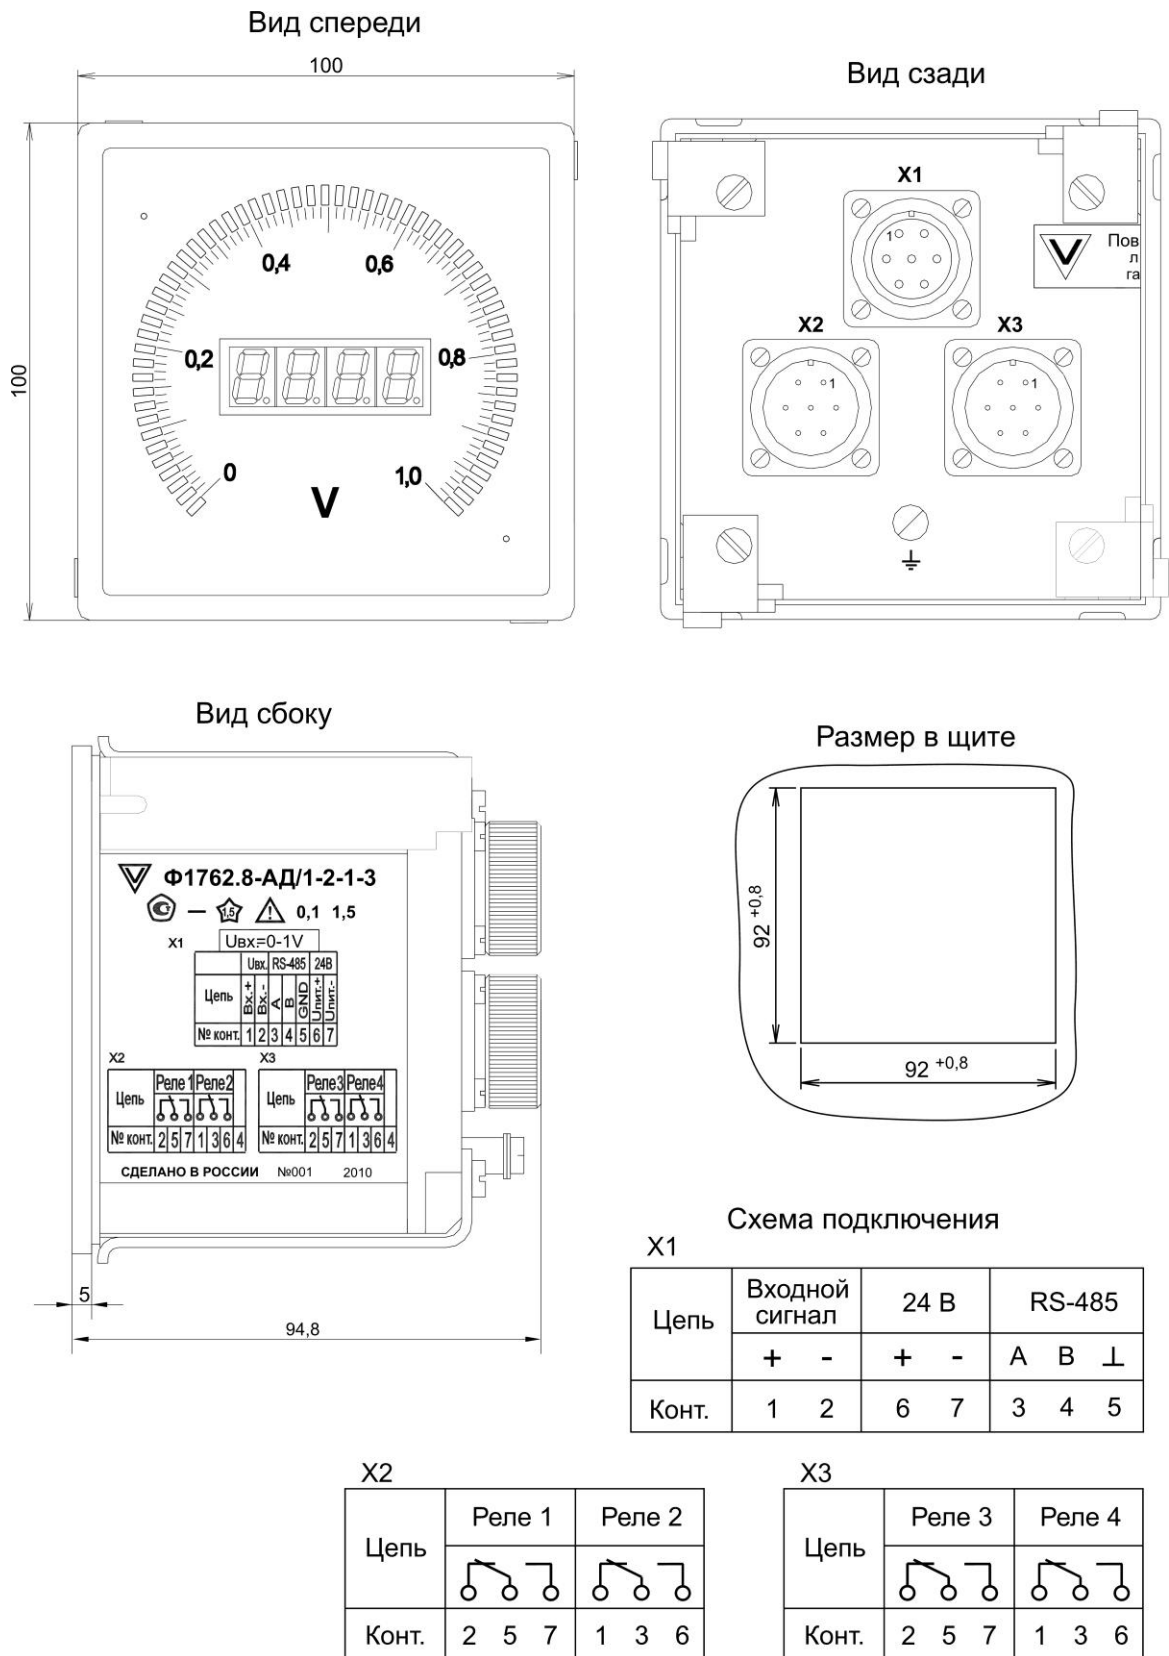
Внешний вид и конструктив прибора, разметка щита и схема подключения прибора Ф1762.8-АД/1-х-х-3
